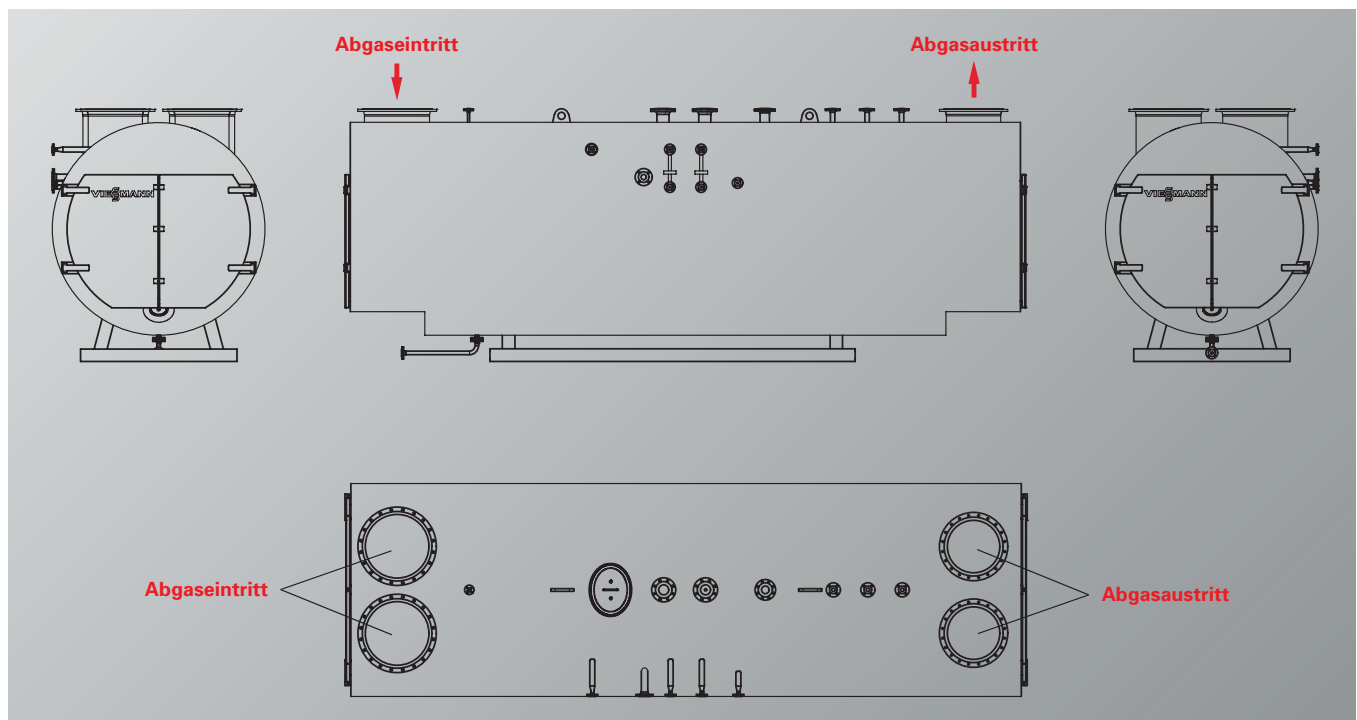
1-Zug-Abhitzekessel zur Dampferzeugung für zwei Abgasquellen (Alle weiteren Kesselanschlüsse entsprechen den konventionellen Dampf- bzw. Heißwassererzeugern).
